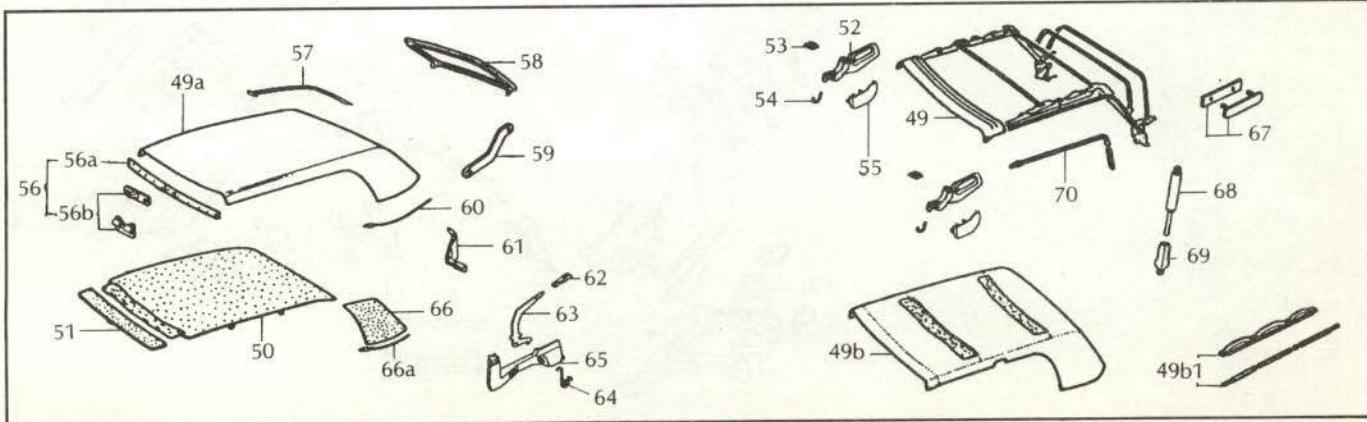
Elementos de la capota que comercializa el fabricante.
